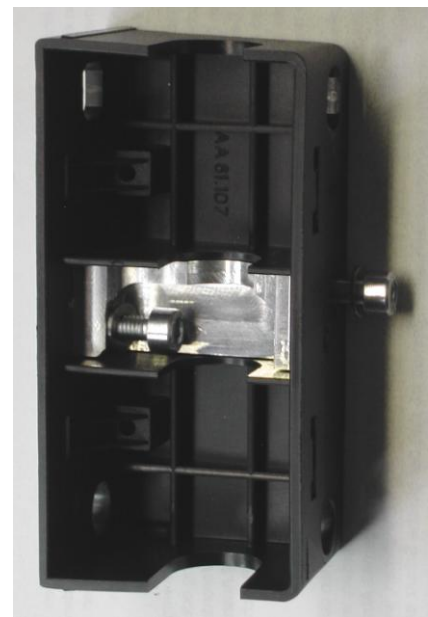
Mit einem Stück Aluminium verstärkter Grundkörper der Horizontalverstellung
